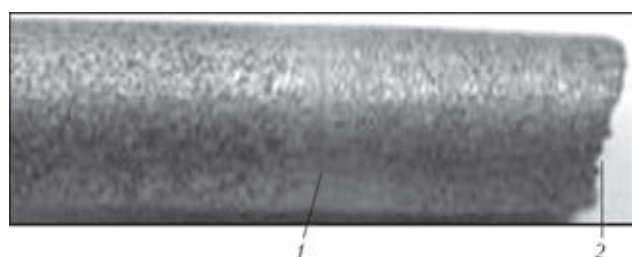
Вид образца после испытаний на растяжение: 1 — сварной шов; 2 — зона разрушения
